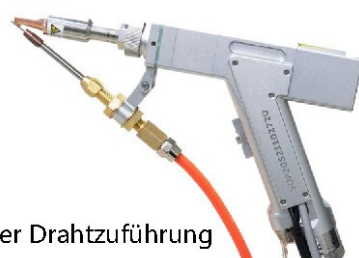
Schweißpistole mit einfacher Drahtzuführung
